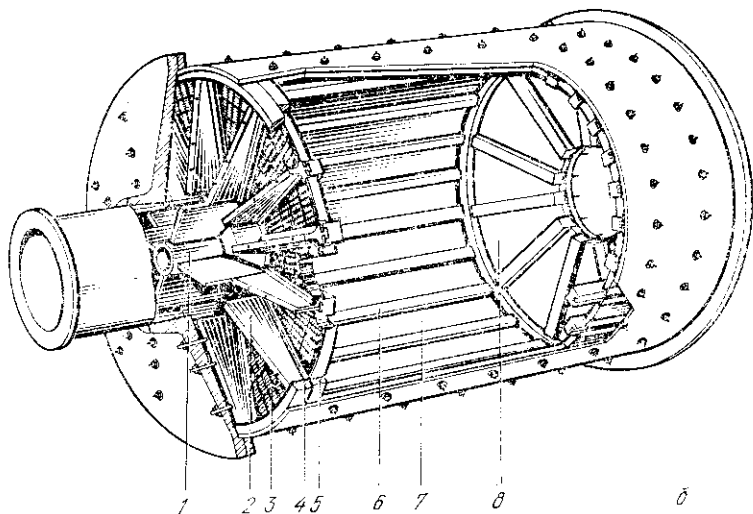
Резиновая футеровка: 1 — футеровка разгрузочной цапфы с центральной втулкой; 2 — ребро-разделительная стенка секции; 3 — разгрузочная решетка; 4 — уплотняющий дуговой брус ребра; 5 — то же, разгрузочной решетки; 6 — брус лифтера; 7 — плита корпуса; 8 — сектор загрузочной крышки
